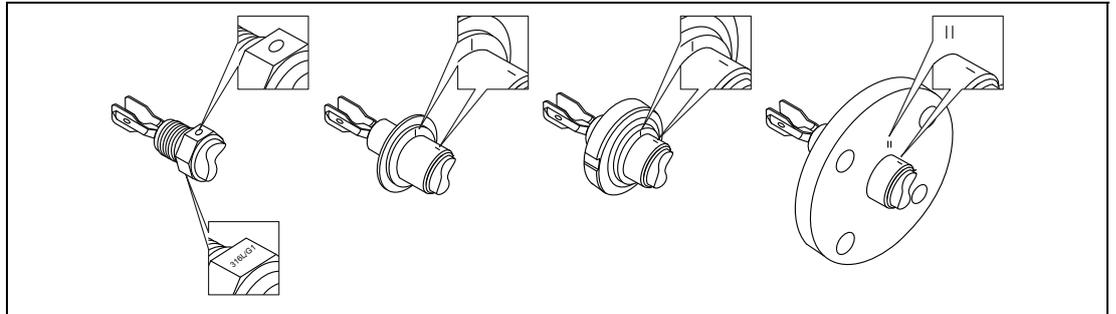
Markierungen für die Ausrichtung der Schwinggabel
